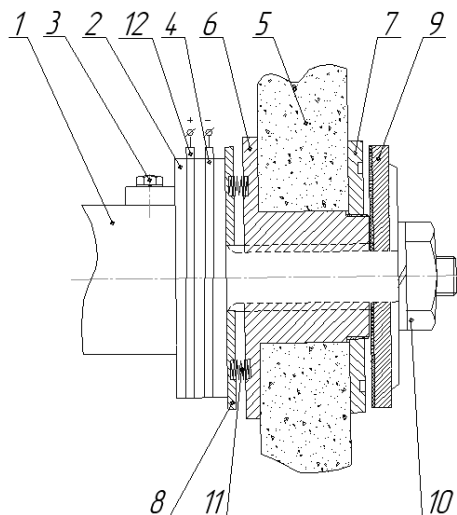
Усовершенствованная головка для реализации шлифования с осевыми колебаниями: 1 – вал; 2 – электромагнитная катушка; 3 – болт; 4 – токосъемник; 5 – шлифовальный круг; 6 – шлицевая втулка; 7, 10 – гайка; 8 – кольцевая шайба; 9 – шайба; 11 – пружина; 12 – щетка.
